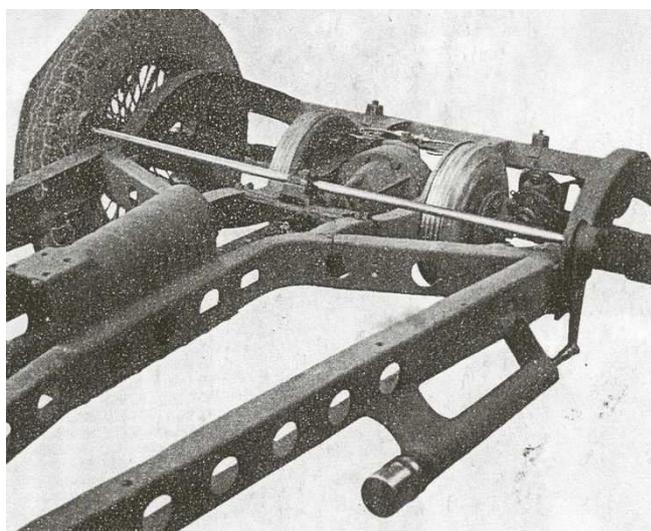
Спортивный автомобиль сороковых годов с задними тормозами, расположенными у главной передачи.
